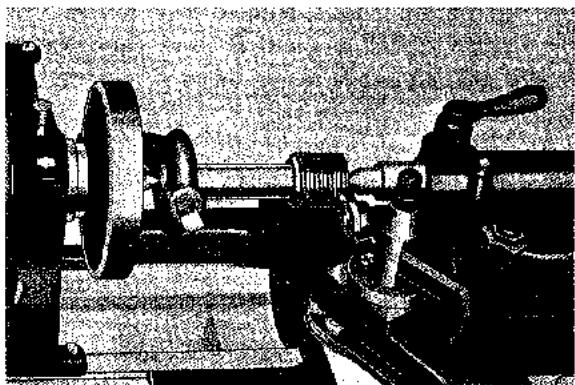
Tallado en el torno de una rosca exterior (South Bend Lathe Works)
